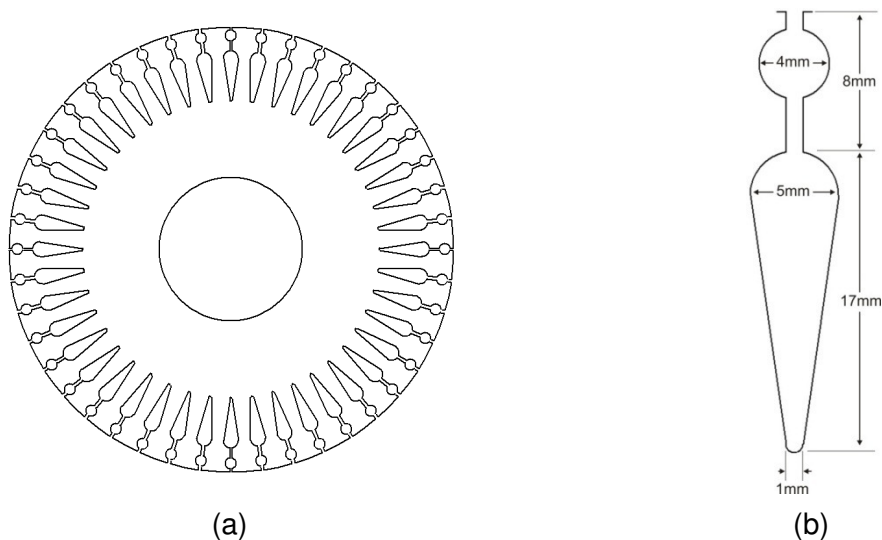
(a) Vista geral do rotor do terceiro motor. (b) Detalhes da ranhura do rotor do motor 3.
